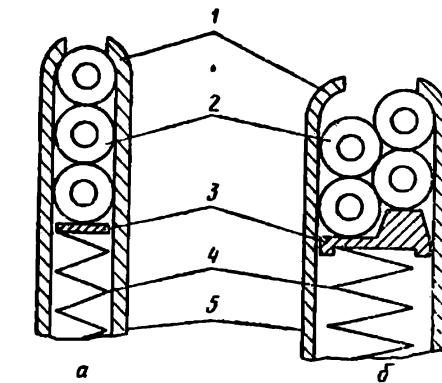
Конструктивные схемы коробчатых магазинов с однорядным (а) и двухрядным (б) расположением патронов:
